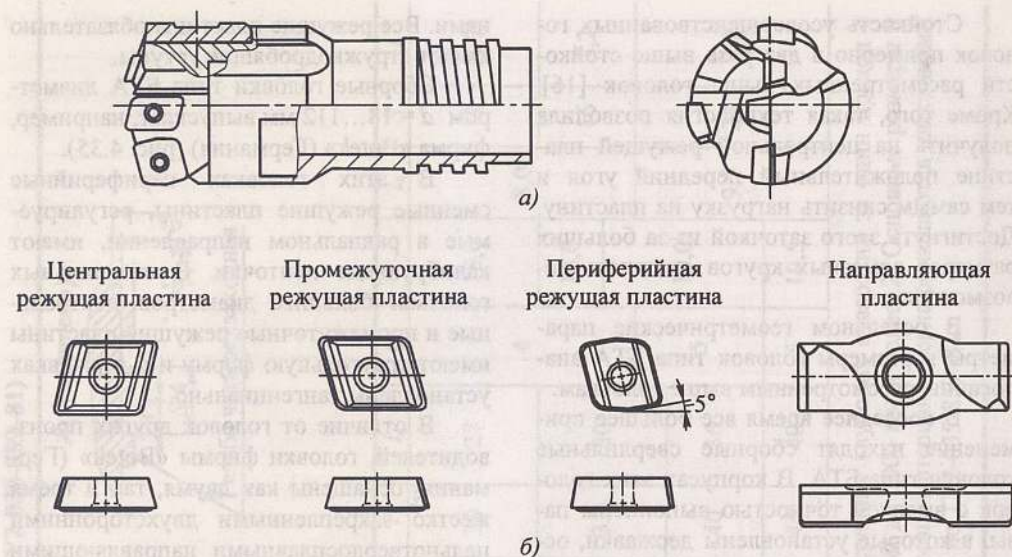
Сборная сверлильная головка типа БТА CoroDrill фирмы «Sandvik Coromant» (Швеция): а – общий вид головки; б – твердосплавные сменные режущие и направляющие пластины
